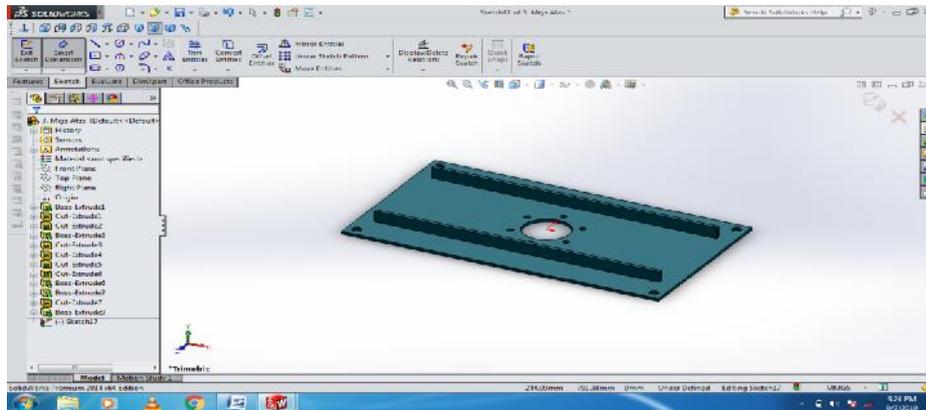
Desain plat atas dudukan *jack hydraulic* pandangan samping
